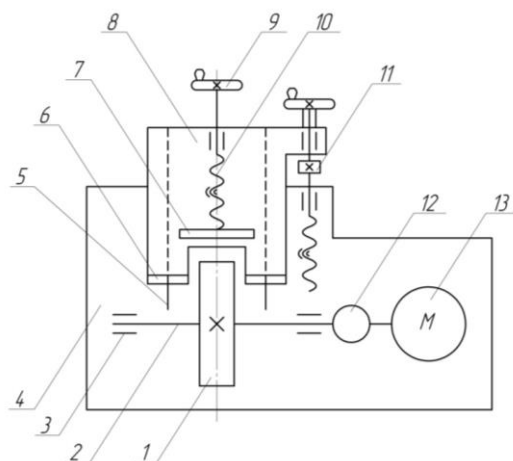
Кинематическая схема экспериментальной установки: 1 – диск с ножами; 2 – вал; 3 – подшипниковый узел; 4 – станина; 5 – направляющая опора; 6 – упорная пластина; 7 – прижимная плита; 8 – салазки; 9 – маховичок; 10 – винт с гайкой; 11 – диск; 12 – динамометрическое устройство; 13 – электродвигатель
